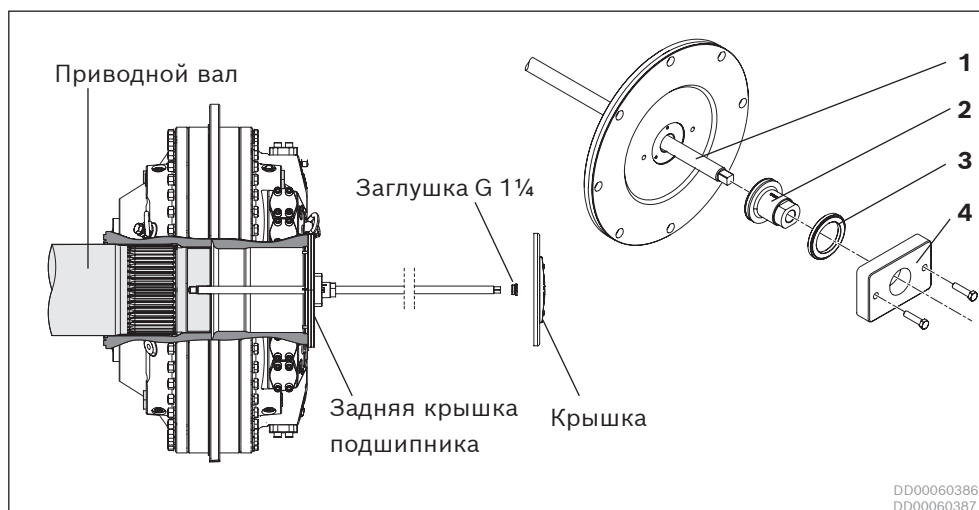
Оправка для демонтажа мотора CBm, оснащенного шлицевым валом
